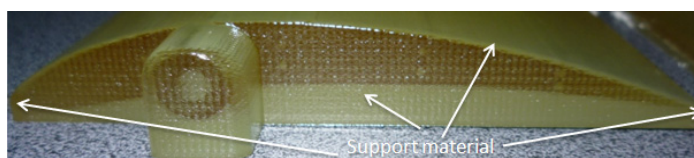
Specimen fabricat aditiv cu tipul de finisare mat [25].
